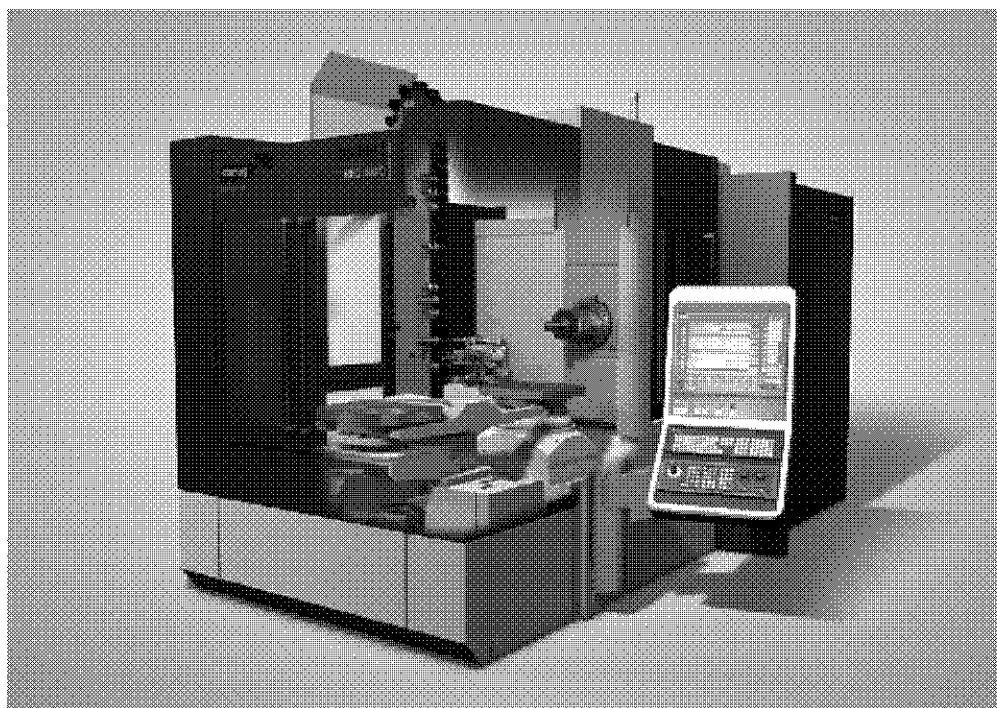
Горизонтальный обрабатывающий центр Heckert HEC 400 D
